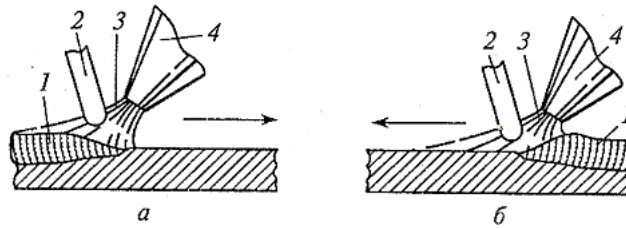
Основные способы газовой сварки: а – правый способ газовой сварки; б – левый способ газовой сварки; 1 – формирующий шов; 2 – присадочный пруток; 3 – пламя горелки; 4 – горелка
